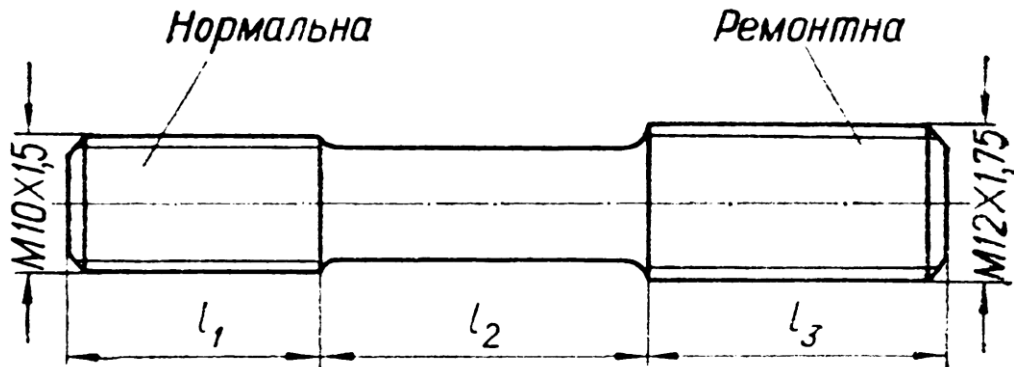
Шпилька ремонтного розміру (ступінчаста)
